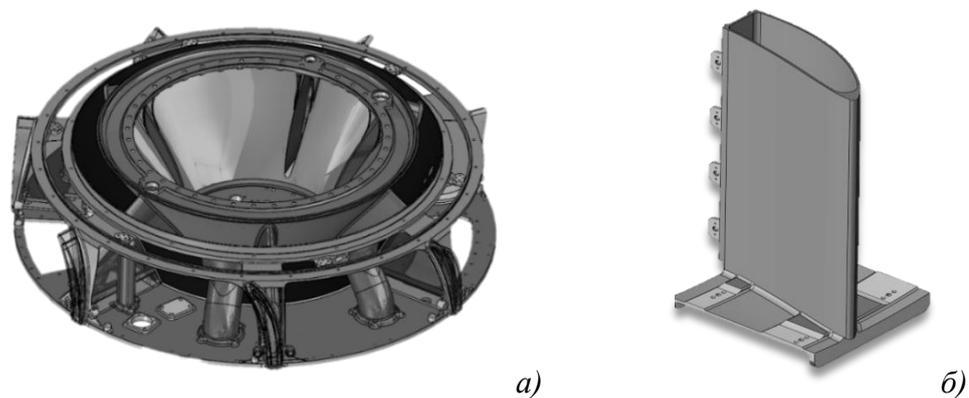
Отливки из сплава VT20Л: а - «Втулка», б - «Стойка»
